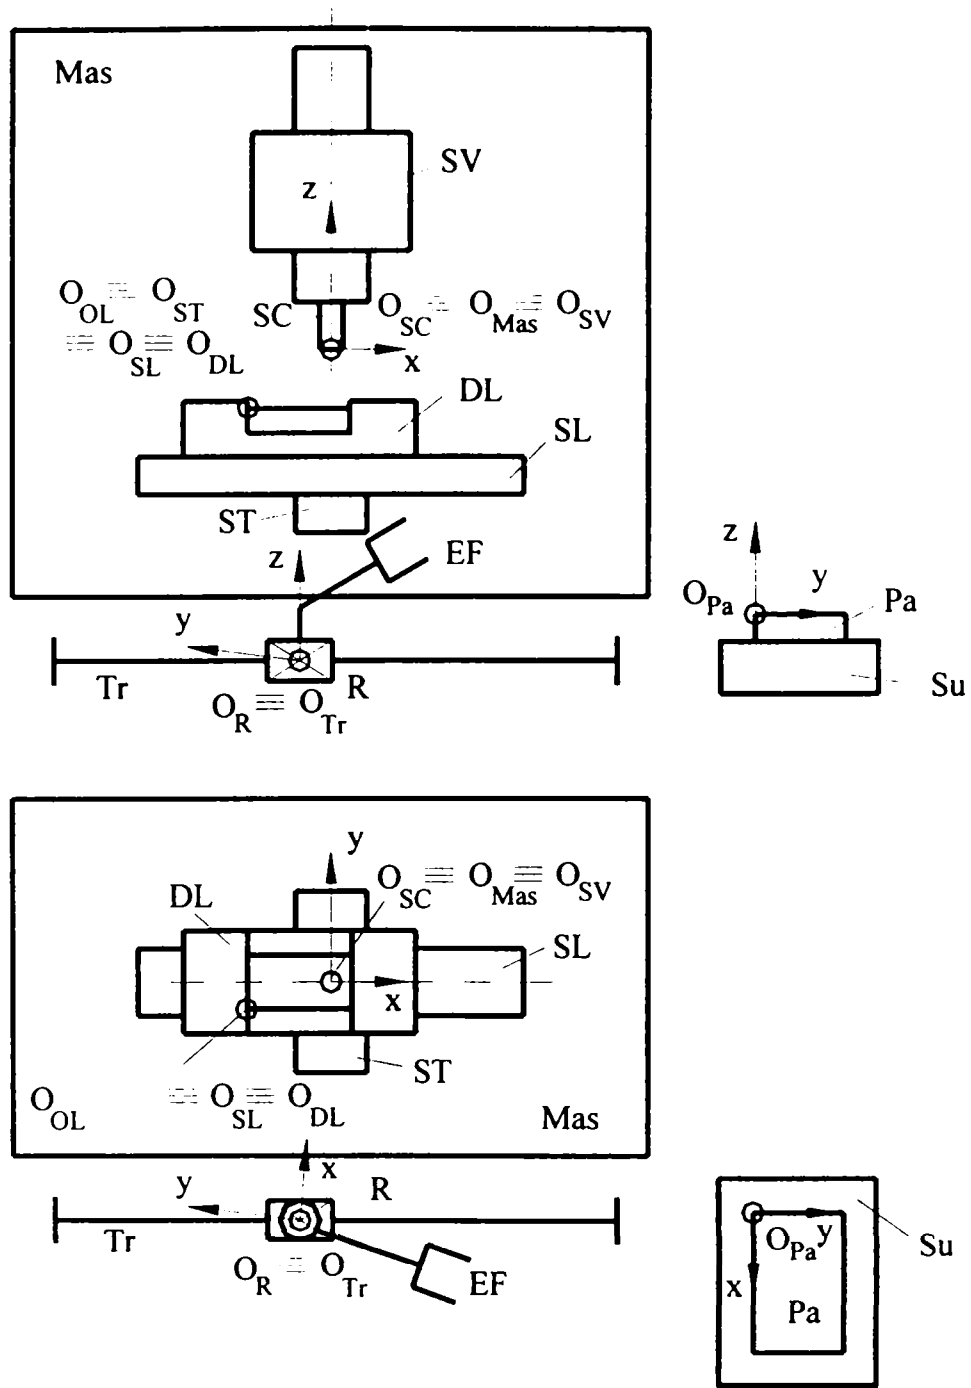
Layout-ul sistemului de fabricație flexibilă ESHED ROBOTEC
